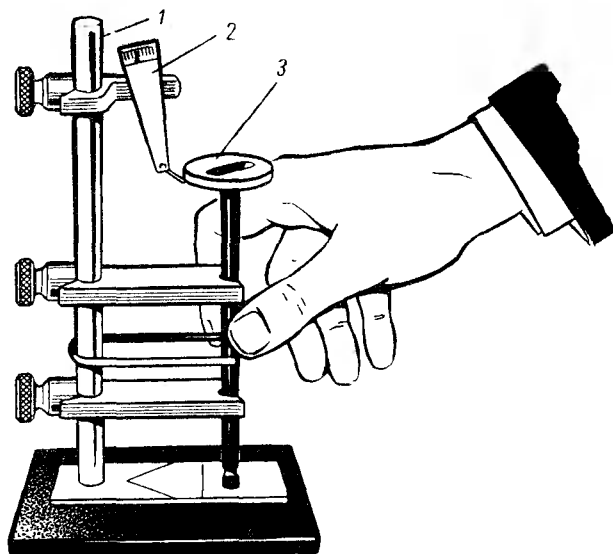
Приспособление для проверки прямолинейности стержня и биения посадочного конуса клапана:
